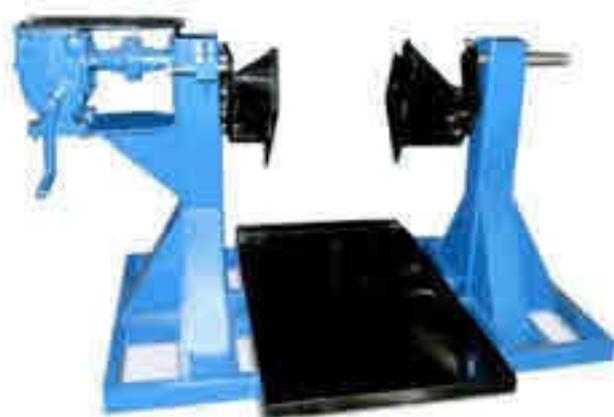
Стенд Р-650 разборки/сборки КПП КамАЗ.
